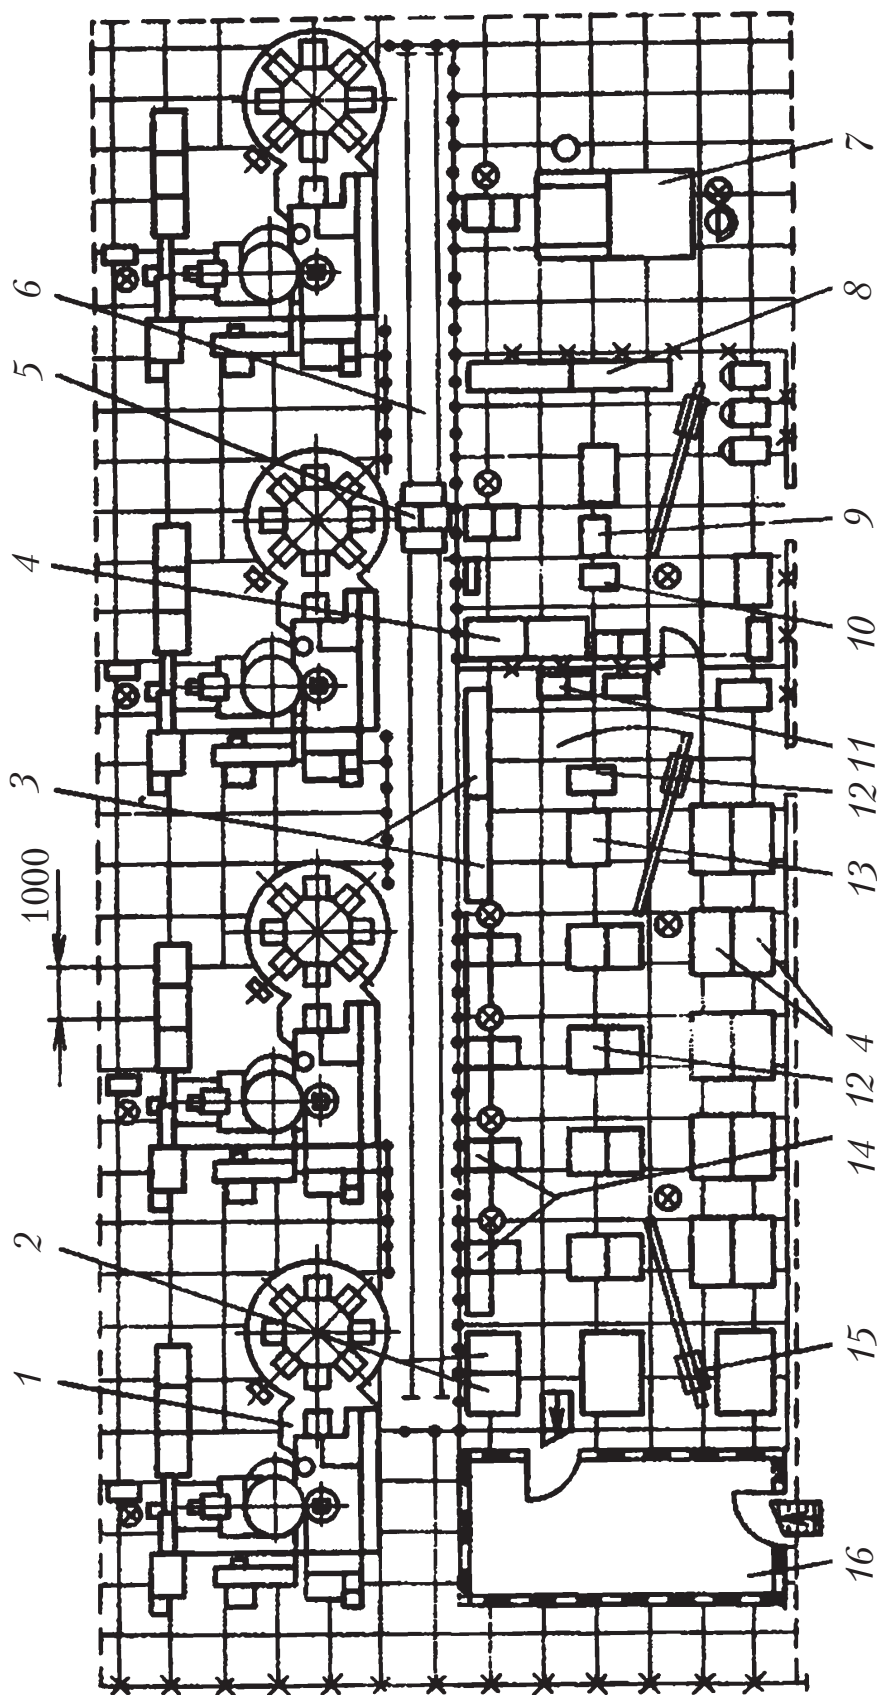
Планировка ГПС АСК-20 для изготовления корпусных деталей станков в условиях мелкосерийного производства
